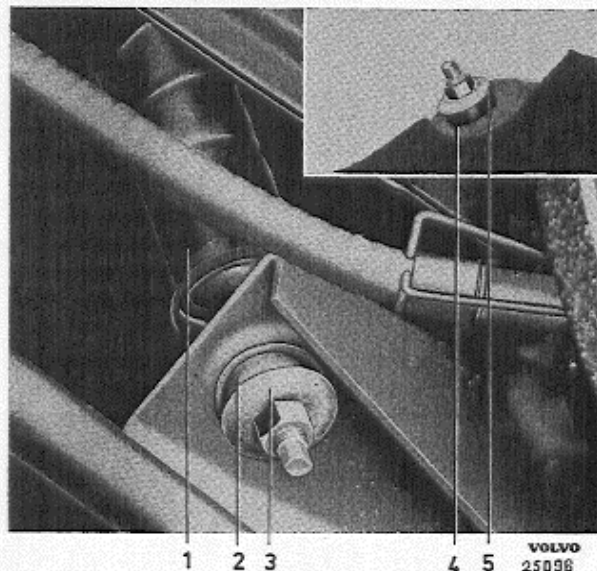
Befestigung des hinteren Stoßdämpfers, P 120
